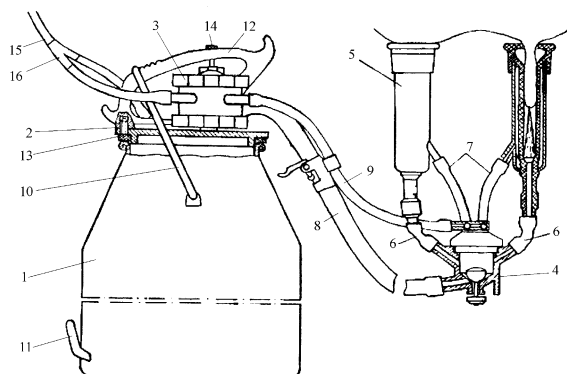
Доильный аппарат АДУ-1: 1 – ведро; 2 – крышка; 3 – пульсатор; 4 – коллектор; 5 – доильные стаканы; 6 – молочные патрубки; 7 – вакуумные патрубки; 8 – шланг молочный; 9 – шланг вакуумный; 10 – дужка; 11 – ручка; 12 – ручка крышки; 13 – прокладка; 14 – винт; 15 – шланг; 16 – двойной патрубок
